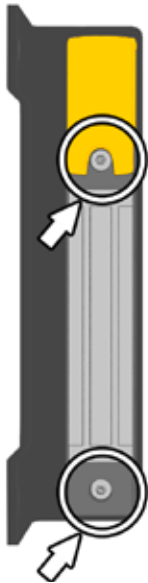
Prozesszuhalterung auf Montageplatte anbringen und Schrauben M6 x 25 mm Torx festziehen.
